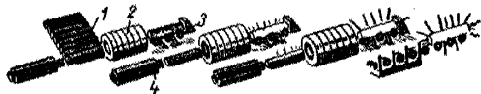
Схема нагревателя, в котором каждая заготовка нагревается последовательно в трех индукторах:
